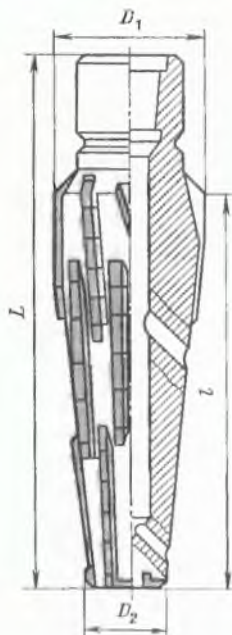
Фрезер-райбер прогрессивного резания типа РПМ
